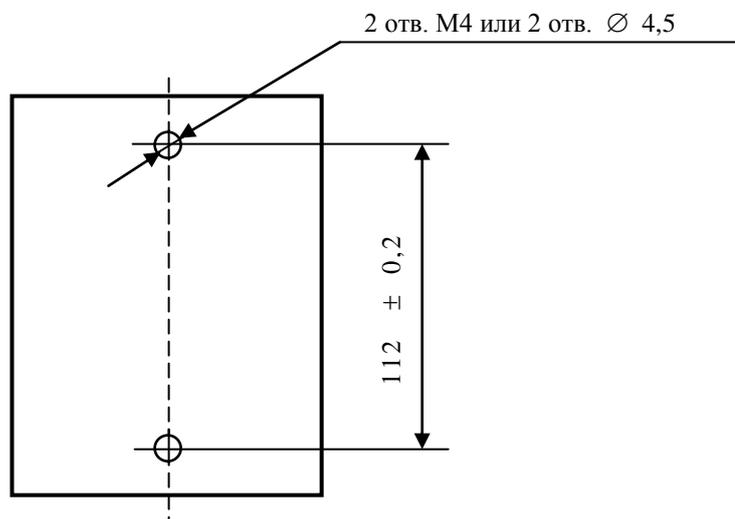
Установка указателя в шкафы, щиты или другое оборудование
